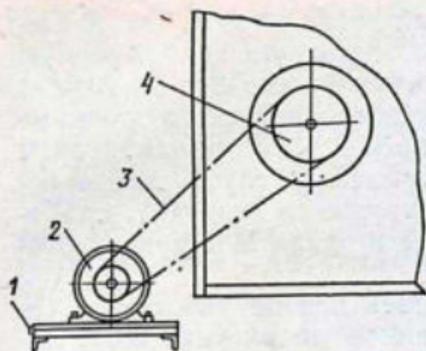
Устройство для натяжения клиновых ремней привода вентилятора:
